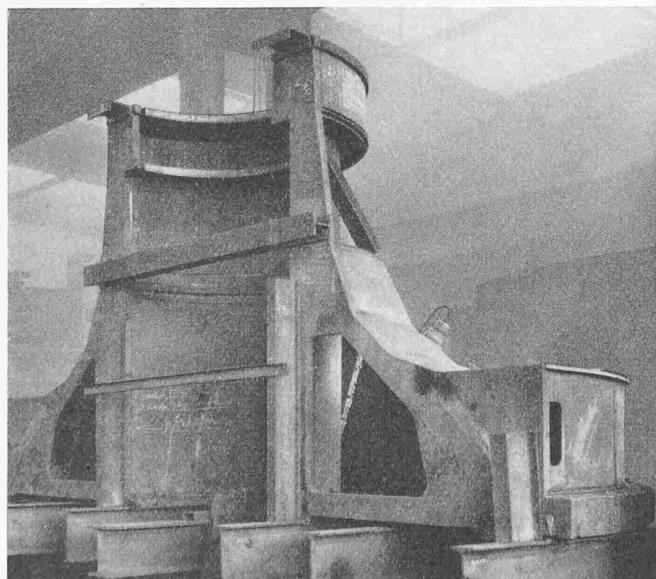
Turbinendeckel beim Schweissen in der Werkstatt
